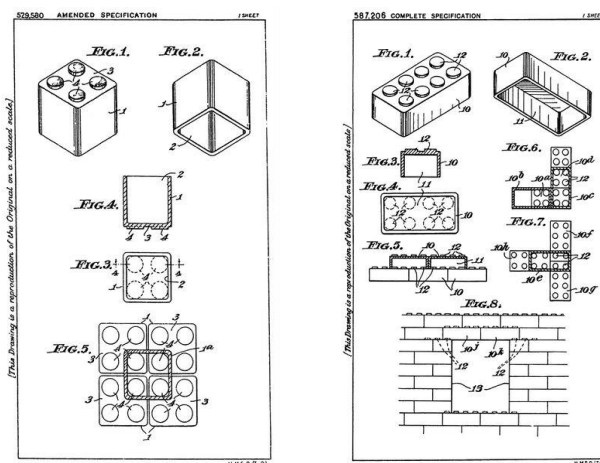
e 65 Patente do *Interlocking Building Cube*; Patente do *Self-Locking Building Brick*.
